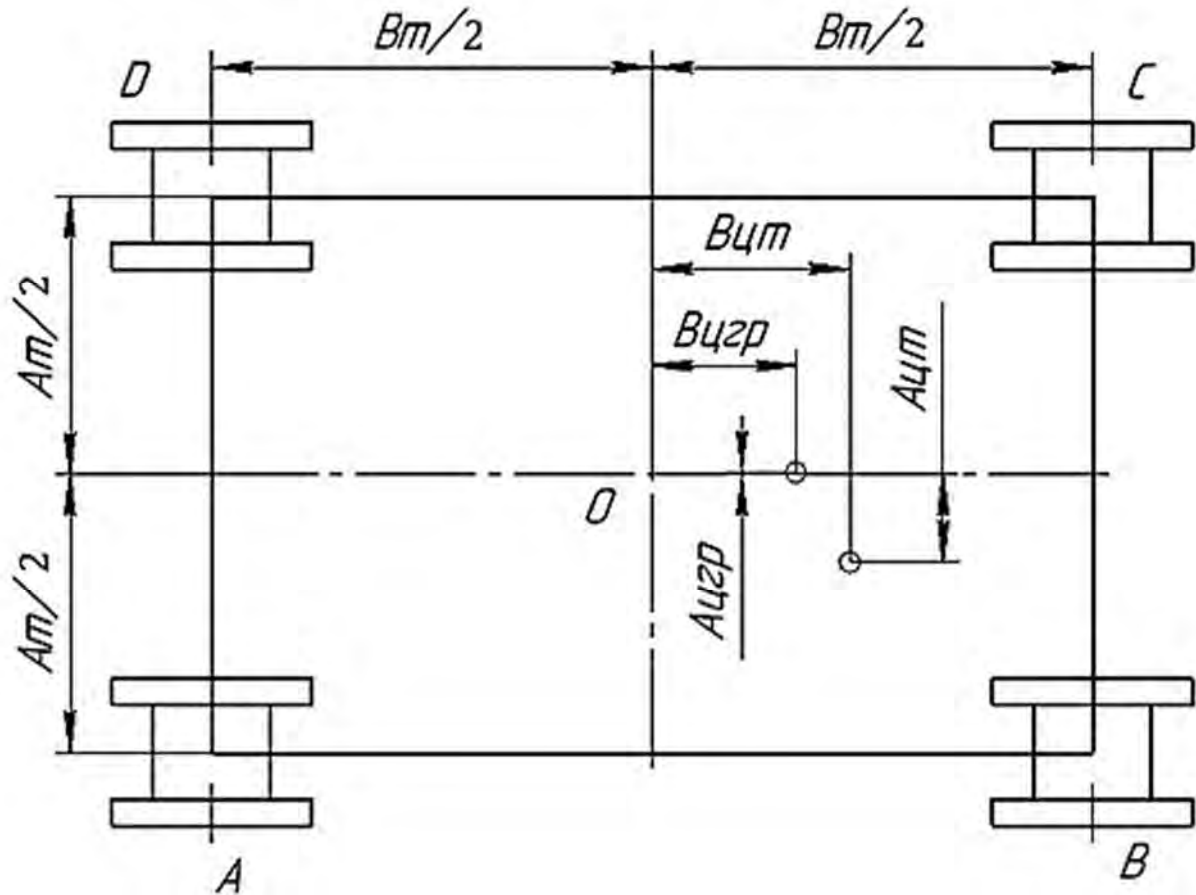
Расчетная схема для определения нагрузок на ходовые колеса
